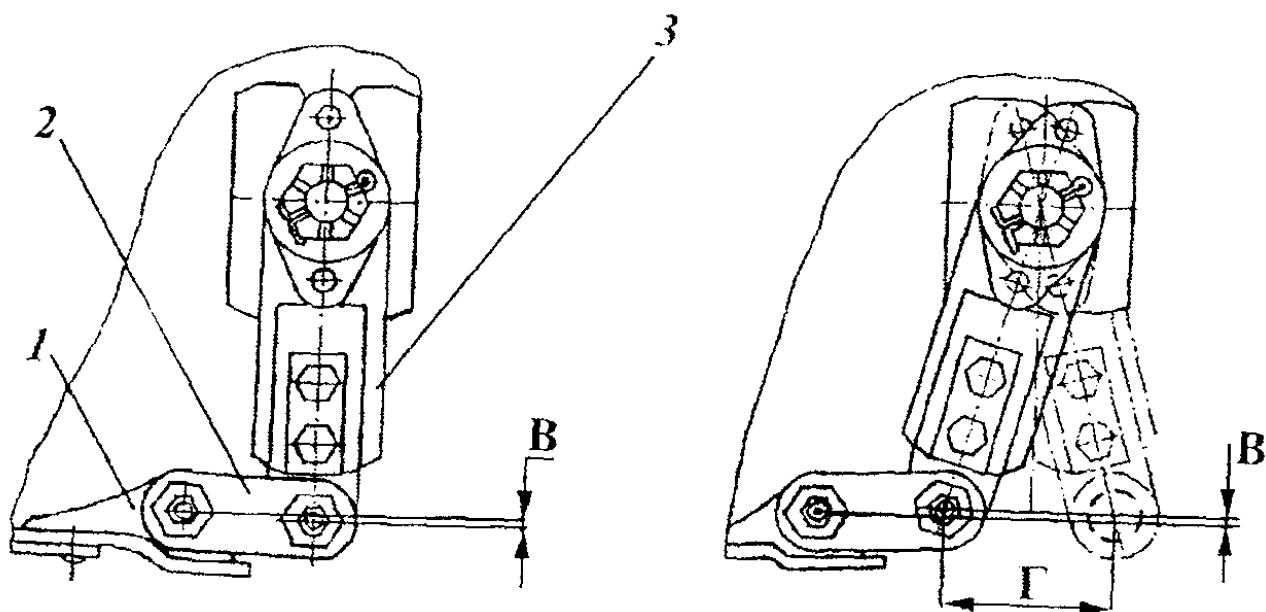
Регулировка привода режущего аппарата: 1 – головка ножа; 2 – щетки; 3 – головка рычага МКШ; А – рычаг МКШ в среднем положении; Б – рычаг МКШ в крайних положениях; В – смещение осей головок ножа и рычага (2,5...3,0 мм); Г – ход ножа (88 мм)
